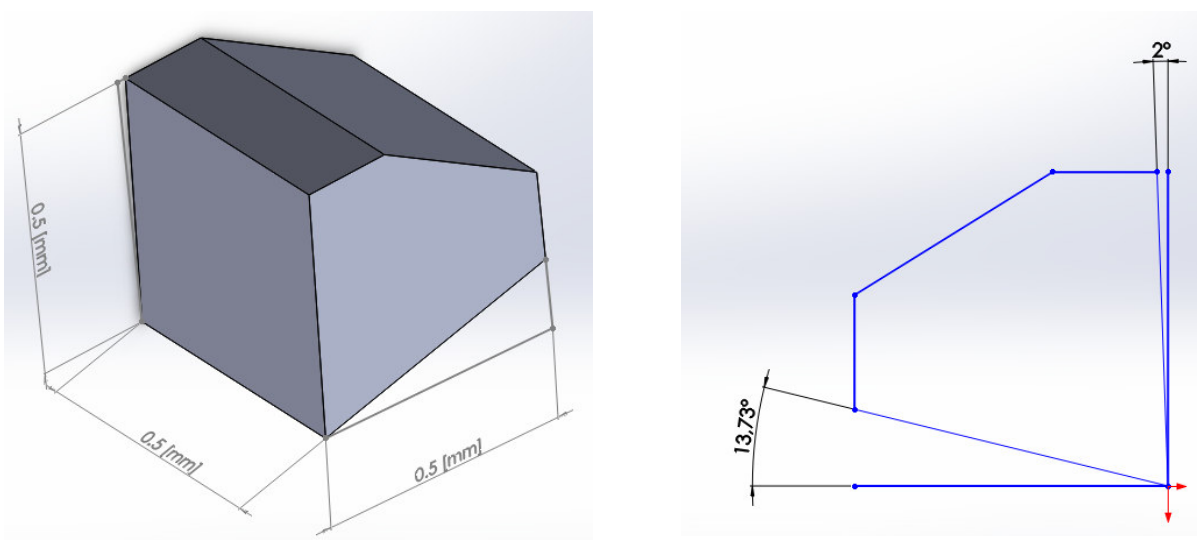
Dimensiones de la herramienta de corte. Ángulos de corte. Dimensión de corte.
